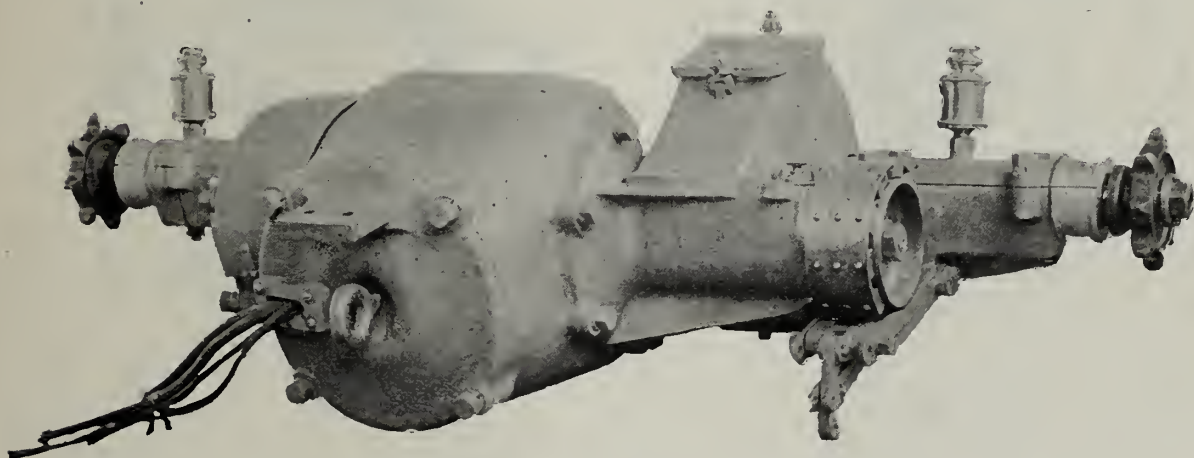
Vue d'ensemble du moteur V2 avec son arbre intermédiaire.
